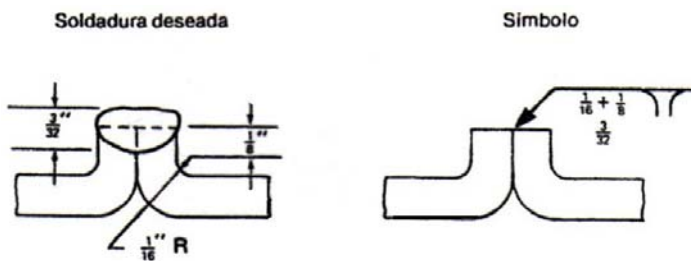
Símbolo de soldadura en el que se especifica una soldadura de borde con radio y altura de la soldadura sobre el punto de tangencia.
